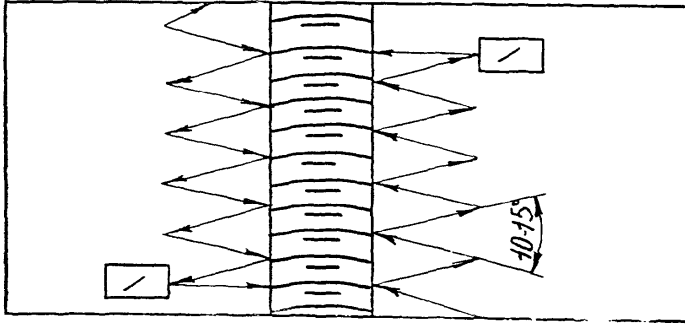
Схема перемещения искателя по поверхности при контроле сварного шва
